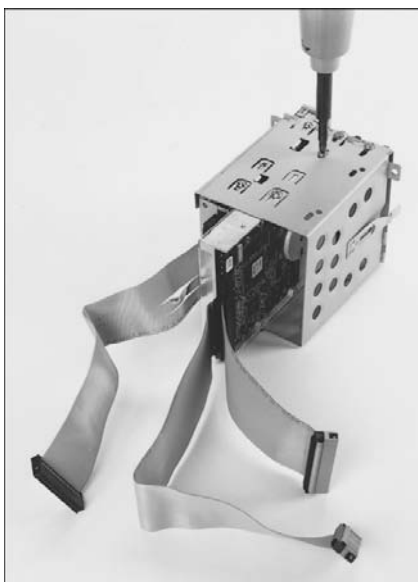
Съемный корпус для установки накопителя в компьютер
